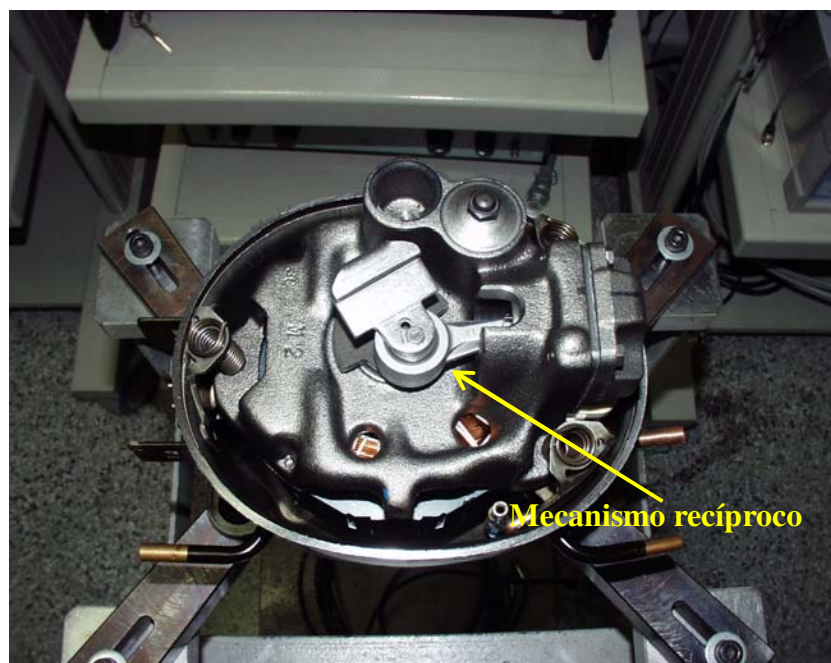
Carcaça aberta de um compressor para a visualização de seu mecanismo recíproco - vista 1.
